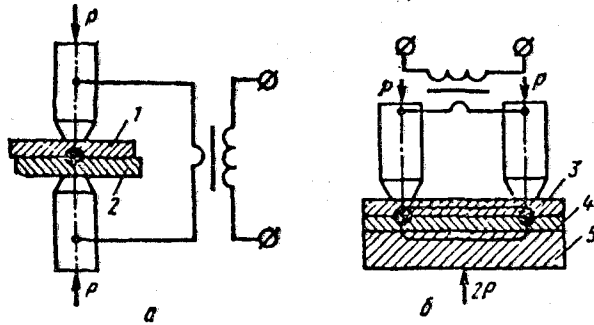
Схема точечной контактной сварки: *а* — двусторонней; *б* — односторонней; 1, 2 — заготовки; 3, 4 — верхний и нижний лист (ток протекает через нижний лист); 5 — токопроводящая медная подкладка
